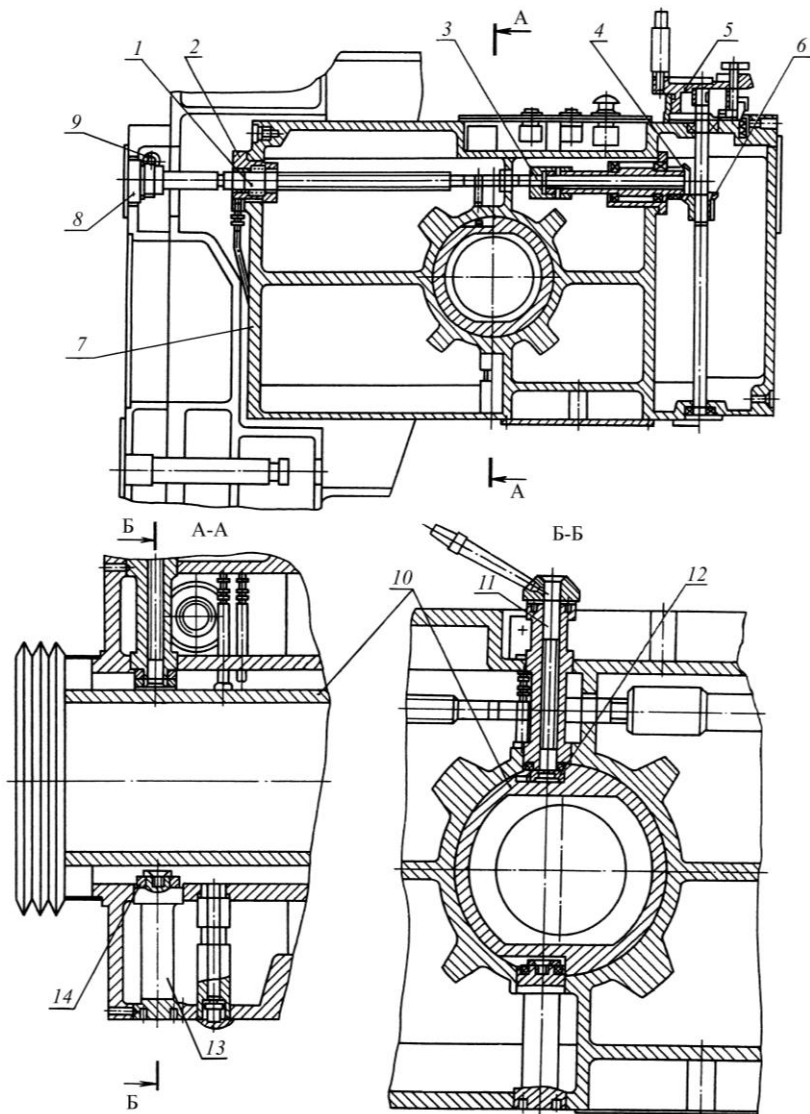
Каретка поперечной подачи шлифовальной бабки универсально-заточного станка модели ЗД642Е
